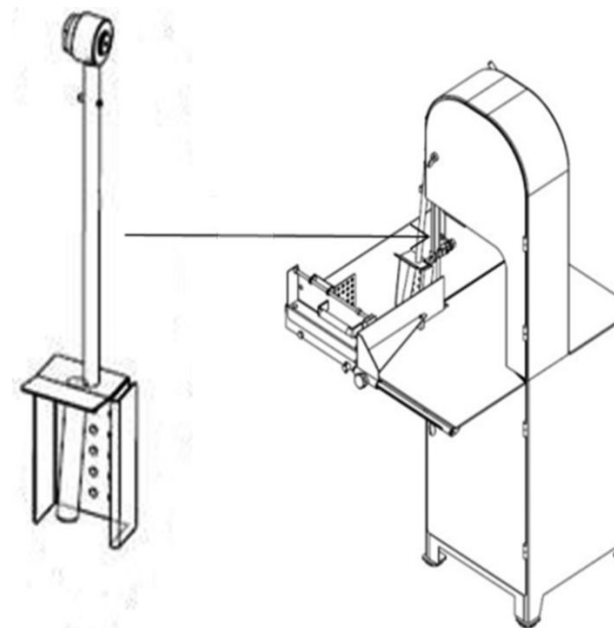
Exemplo de dispositivo para proteção da mão do trabalhador
